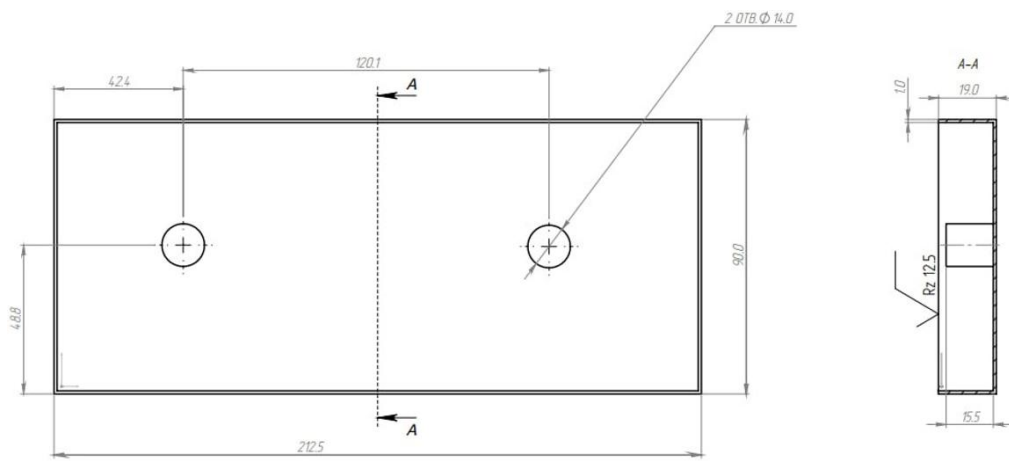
Креслення з розмірами нижньої частини корпусу
